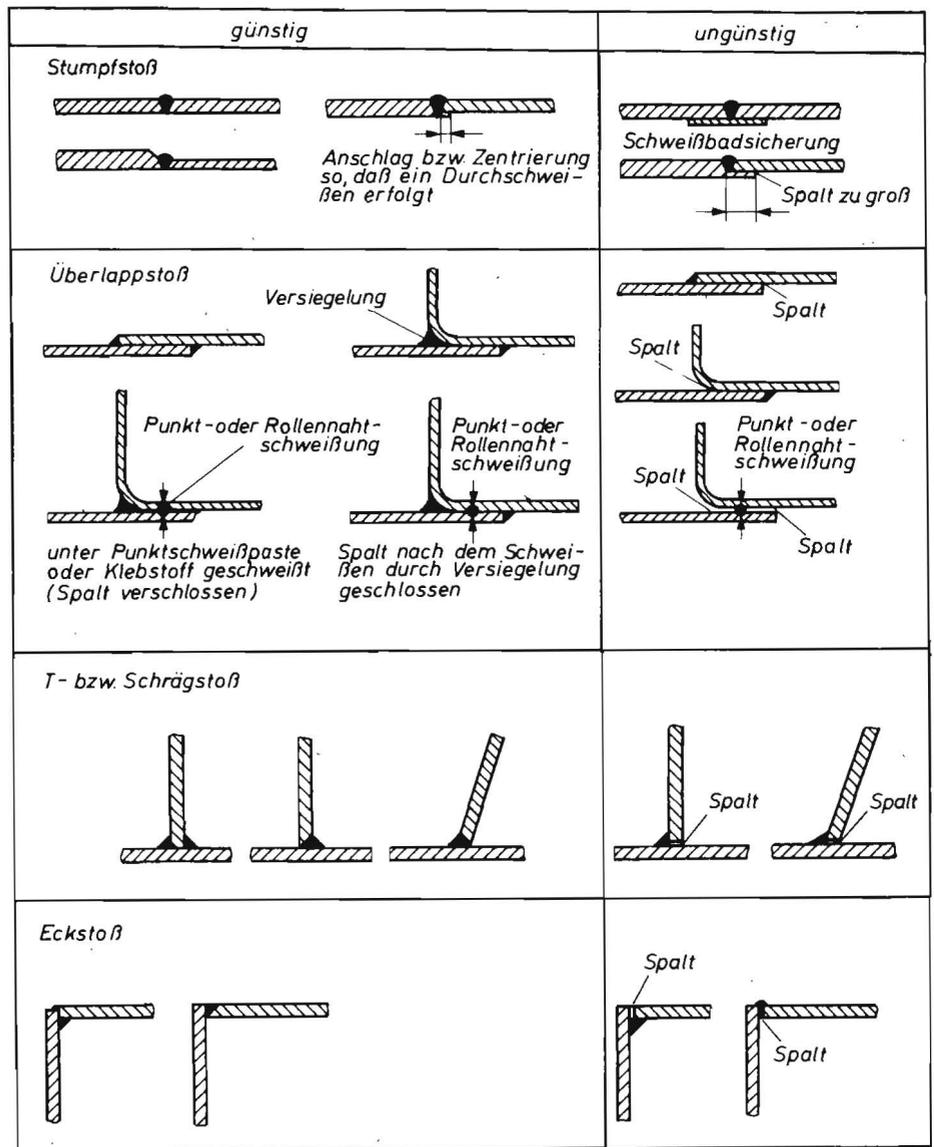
Beispiele für Schweißstoßverbindungen
